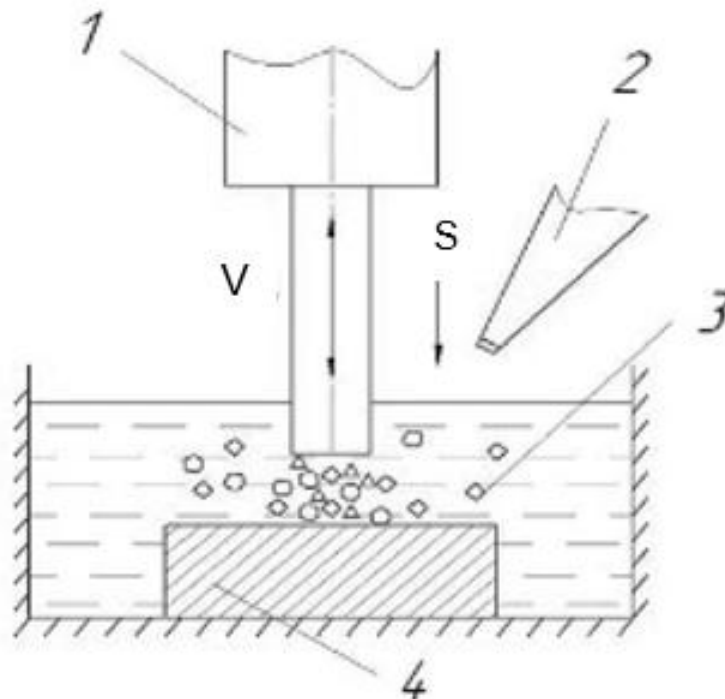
Механизм ультразвуковой обработки керамических материалов: 1-инструмент; 2-насос подачи суспензии абразива; 3-абразив; 4-обрабатываемая деталь
